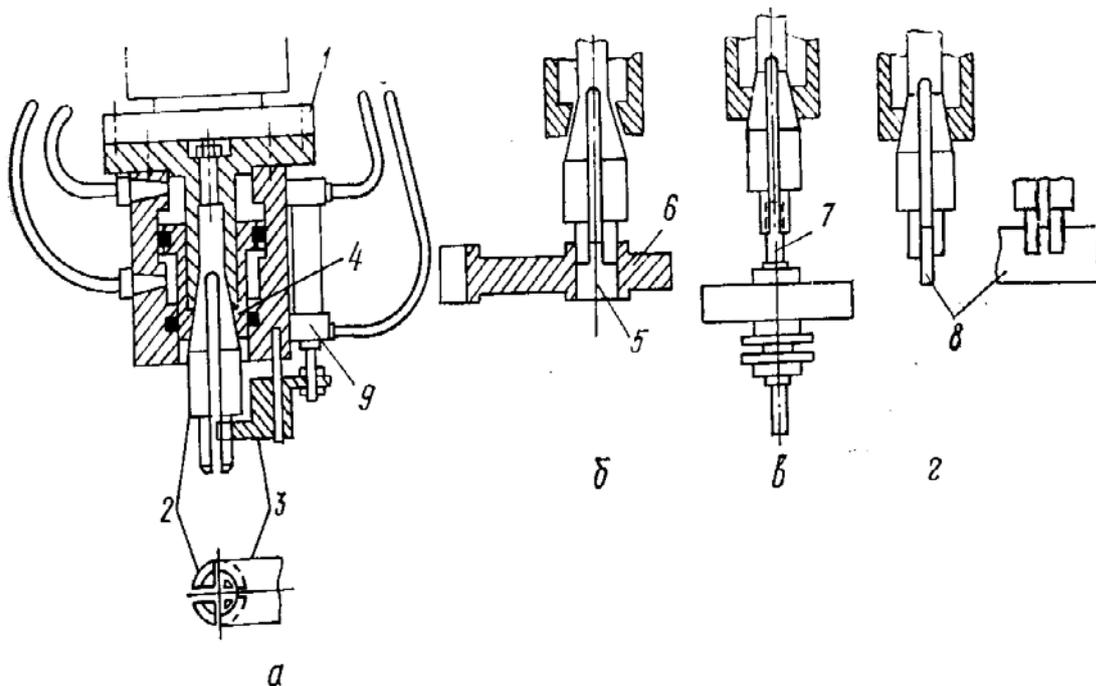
Универсальное захватное устройство с базированием по отверстию детали (а, б), по наружной поверхности (в) и на захвате плоской детали (г)
